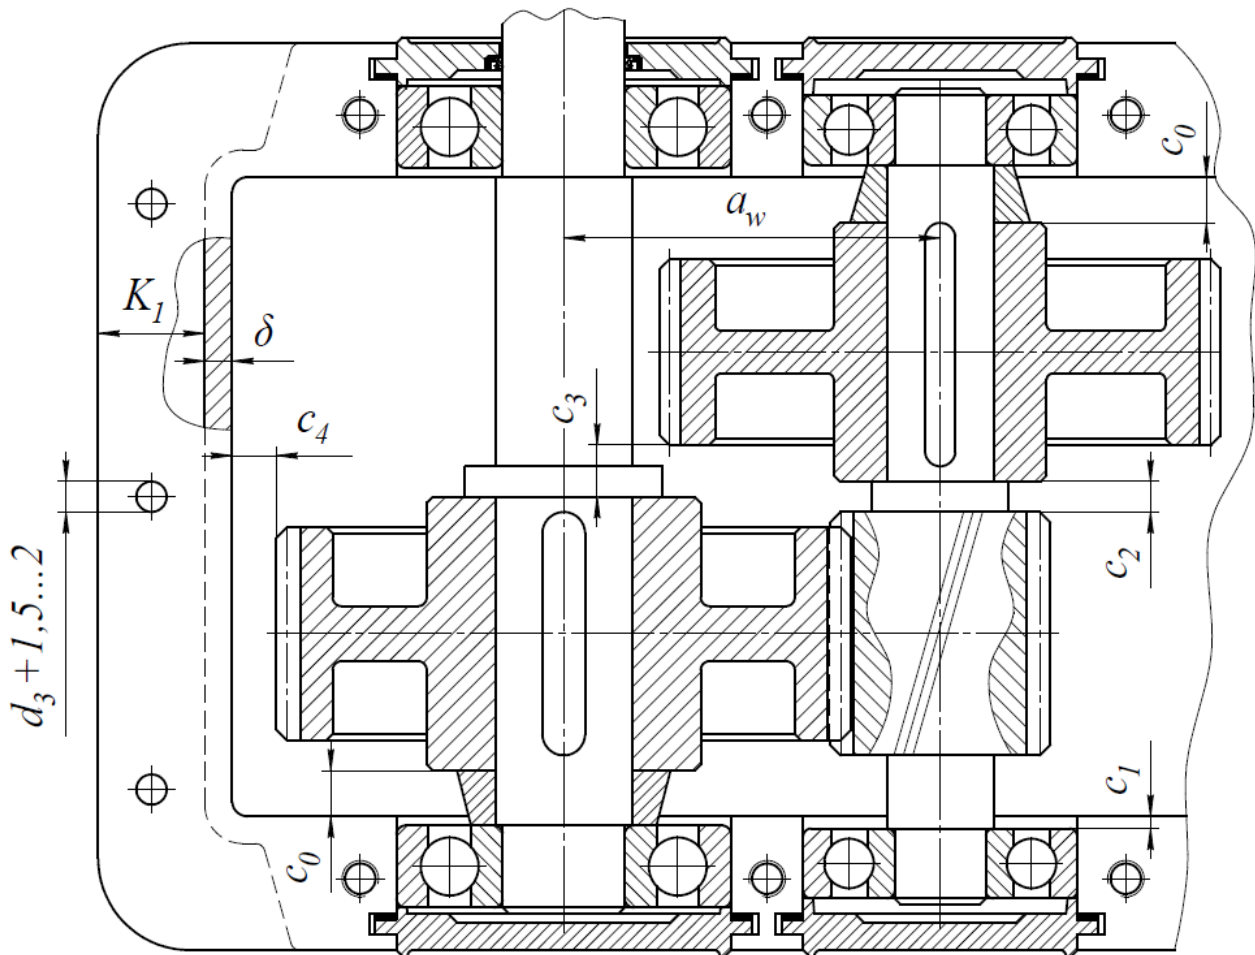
Ескіз розташування передач у корпусі редуктора
